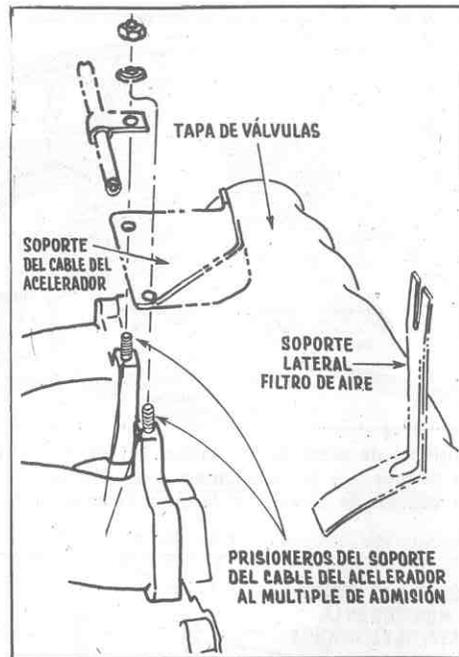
, detalle 1.— Montaje del soporte para el cable de comando del acelerador.
